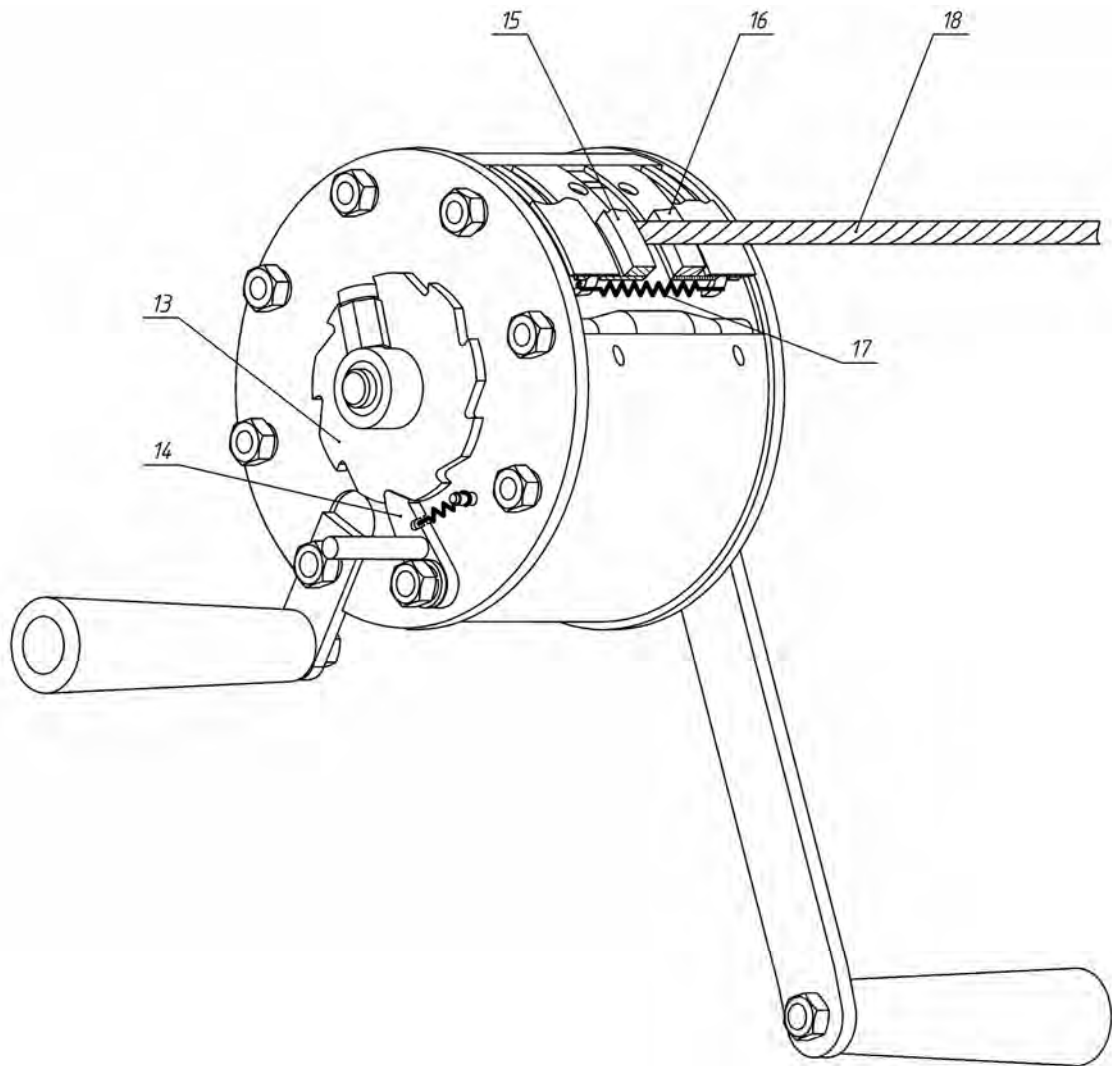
Вид лебедки с элементами стопорения приводного вала и подпружинивания каната
